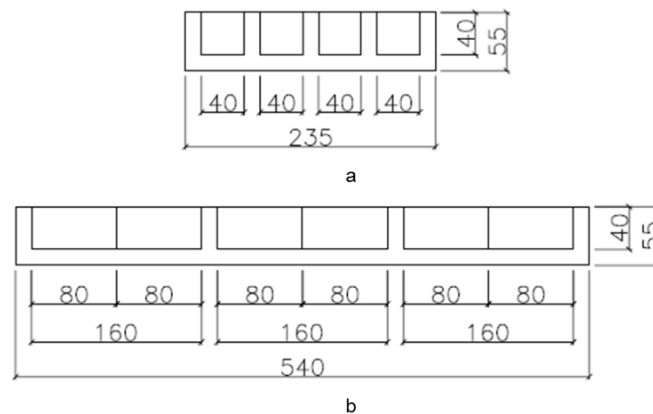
Detalhes da fôrma com dimensões em mm: (a) corte A-A'; (b) corte B-B'.
